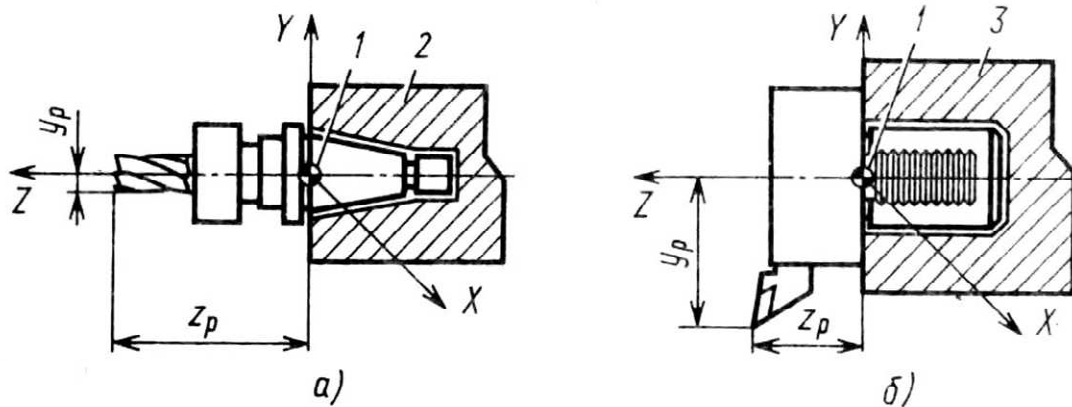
Установка режущего инструмента на многоцелевых ставках: *a* – базирование оправки с фрезой в шпинделе на станке фрезерно-расточного типа; *б* – базирование резцового блока в revolverной головке многоцелевого станка токарного типа; 1 – ноль инструмента; 2 – шпиндель; 3 – revolverная головка
